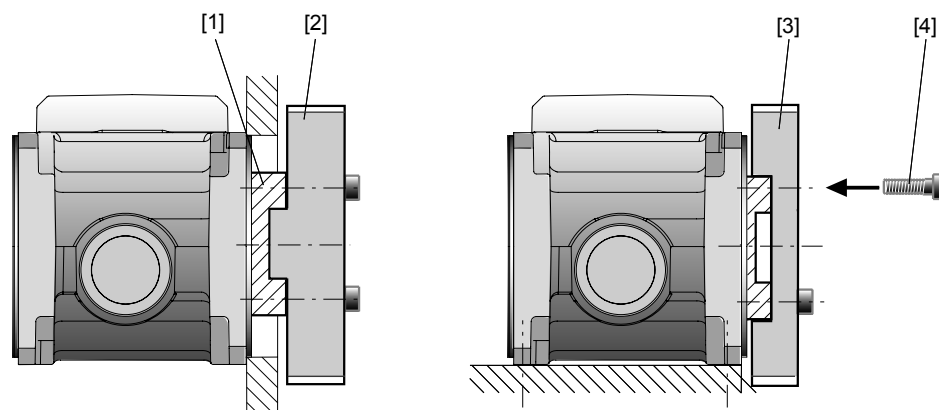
Exemplo de montagem para um bloco de flange BSBF..
